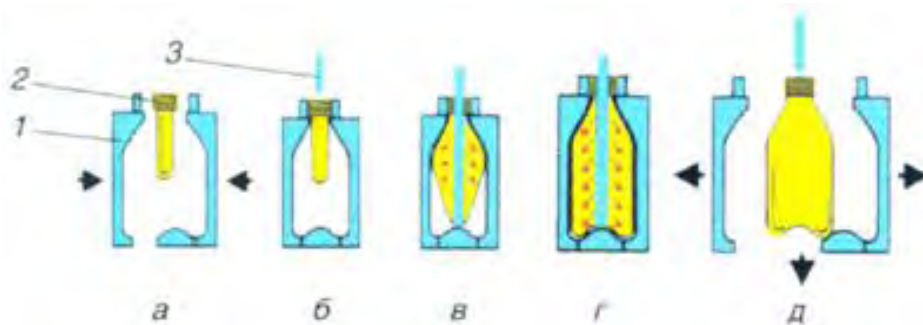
, в. Схема инжекционно-выдвального формования: 1 - пресс-форма; 2 - преформа; 3 - шток
